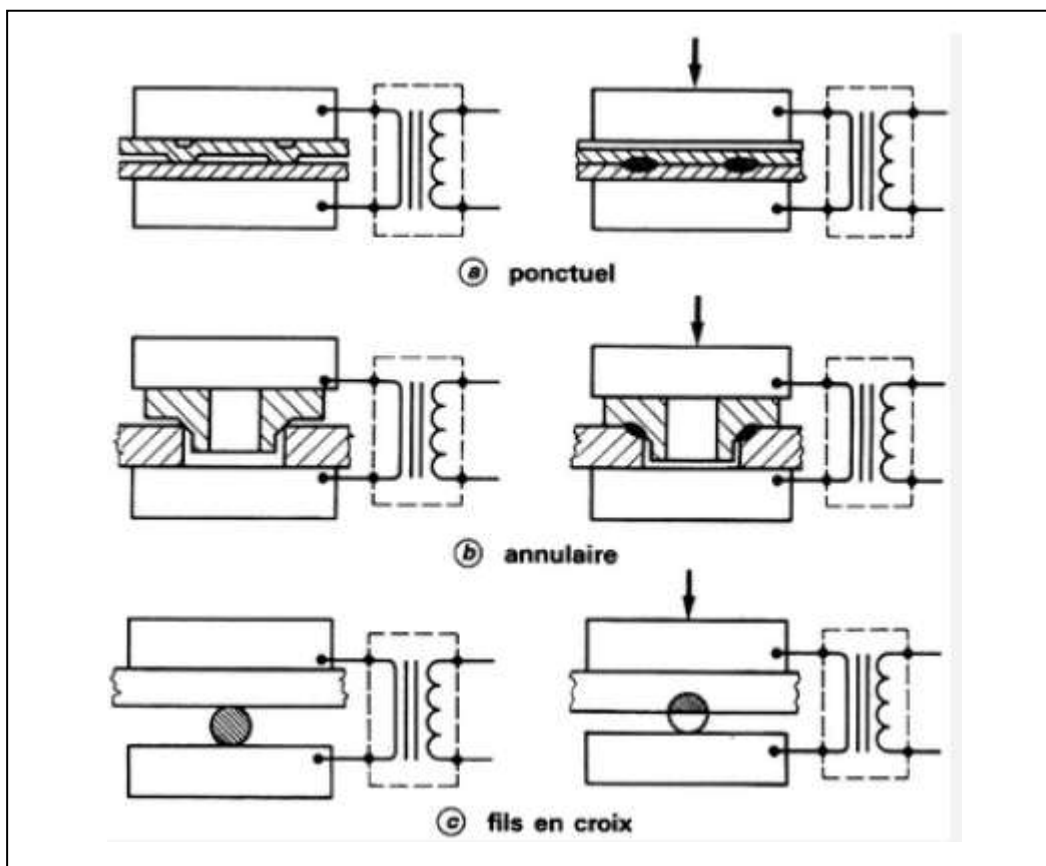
Soudage par bossages : exemples typiques [4]
